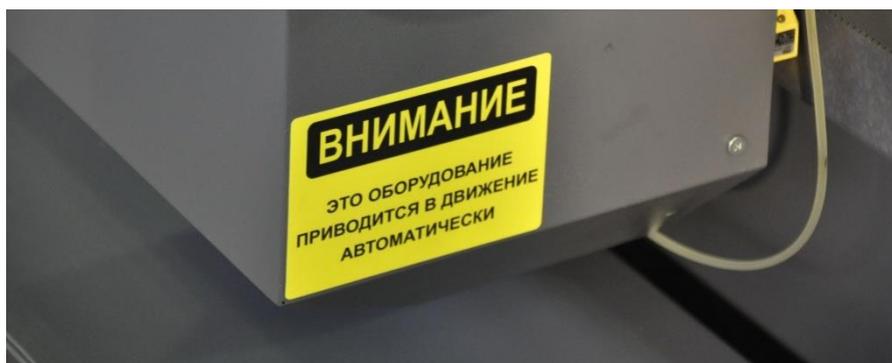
Предупреждающая надпись на корпусе станка с ЧПУ
